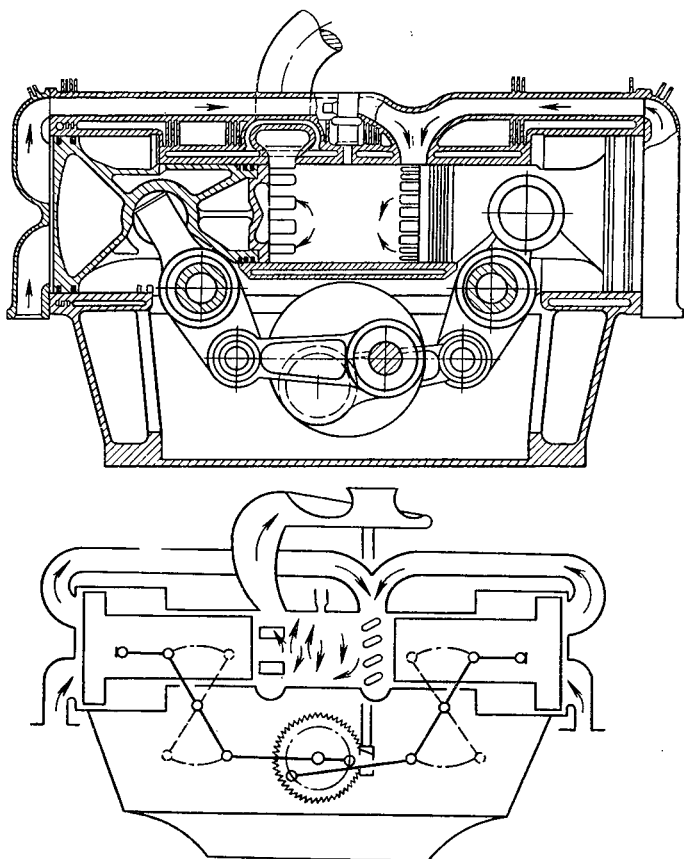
Двухцилиндровый двигатель с регулируемой степенью сжатия
